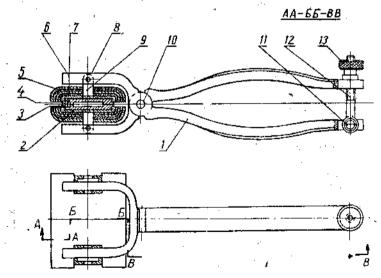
Приспособление для контактной сварки деталей из фторопласта:
